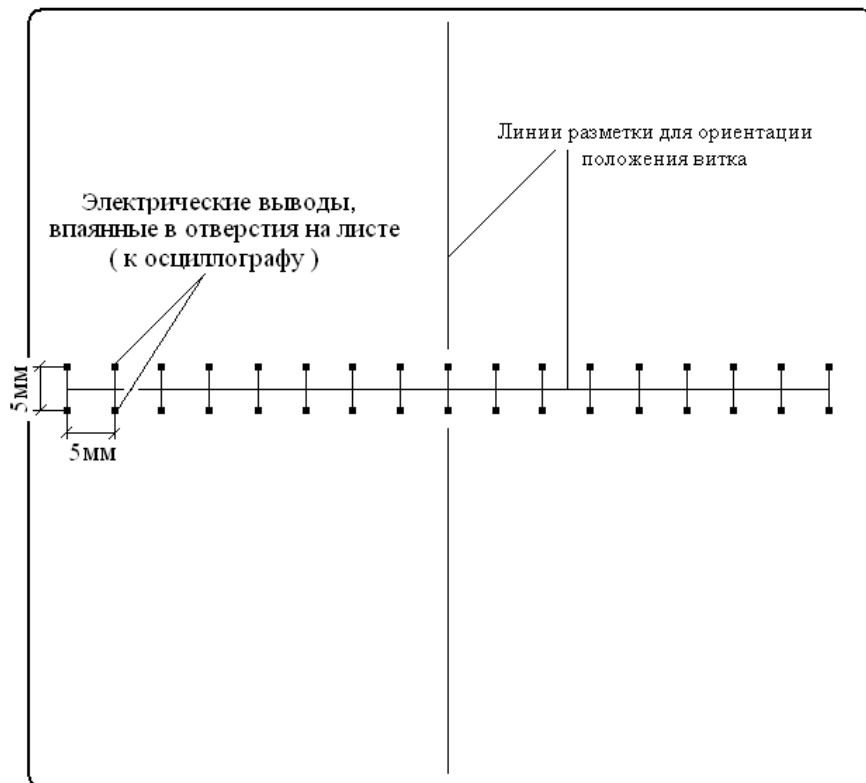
Схематическое изображение листовой заготовки со стороны выводов для проведения измерений
